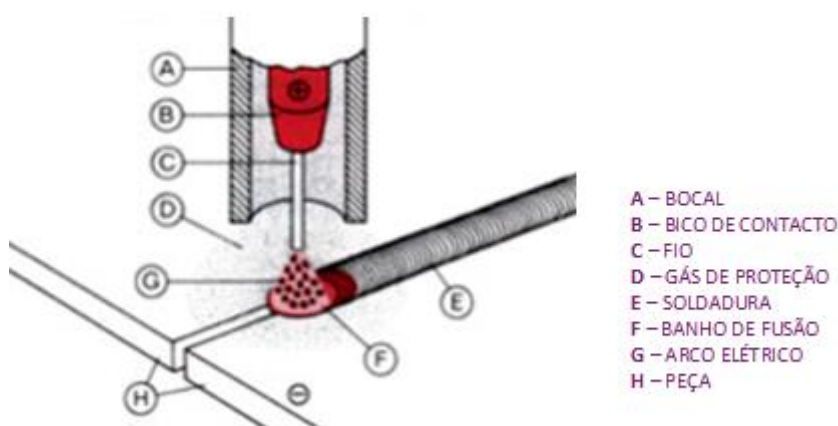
Esquema de soldadura por arco elétrico a gás
